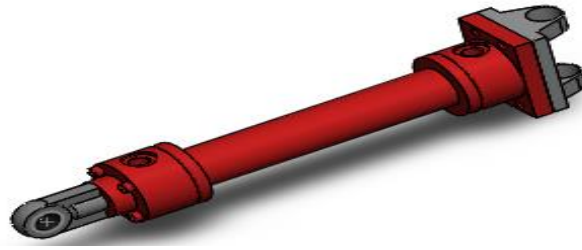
Dessin d'assemblage du vérin hydraulique
